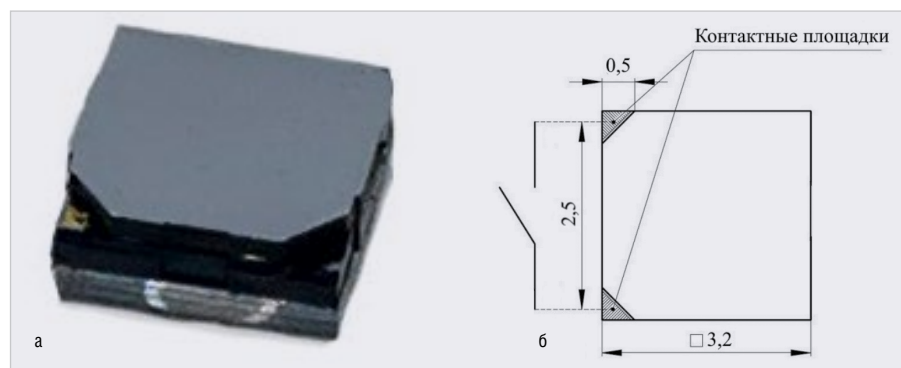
МЭМС датчик удара: а) внешний вид бескорпусного варианта; б) габаритные размеры и эквивалентная схема
